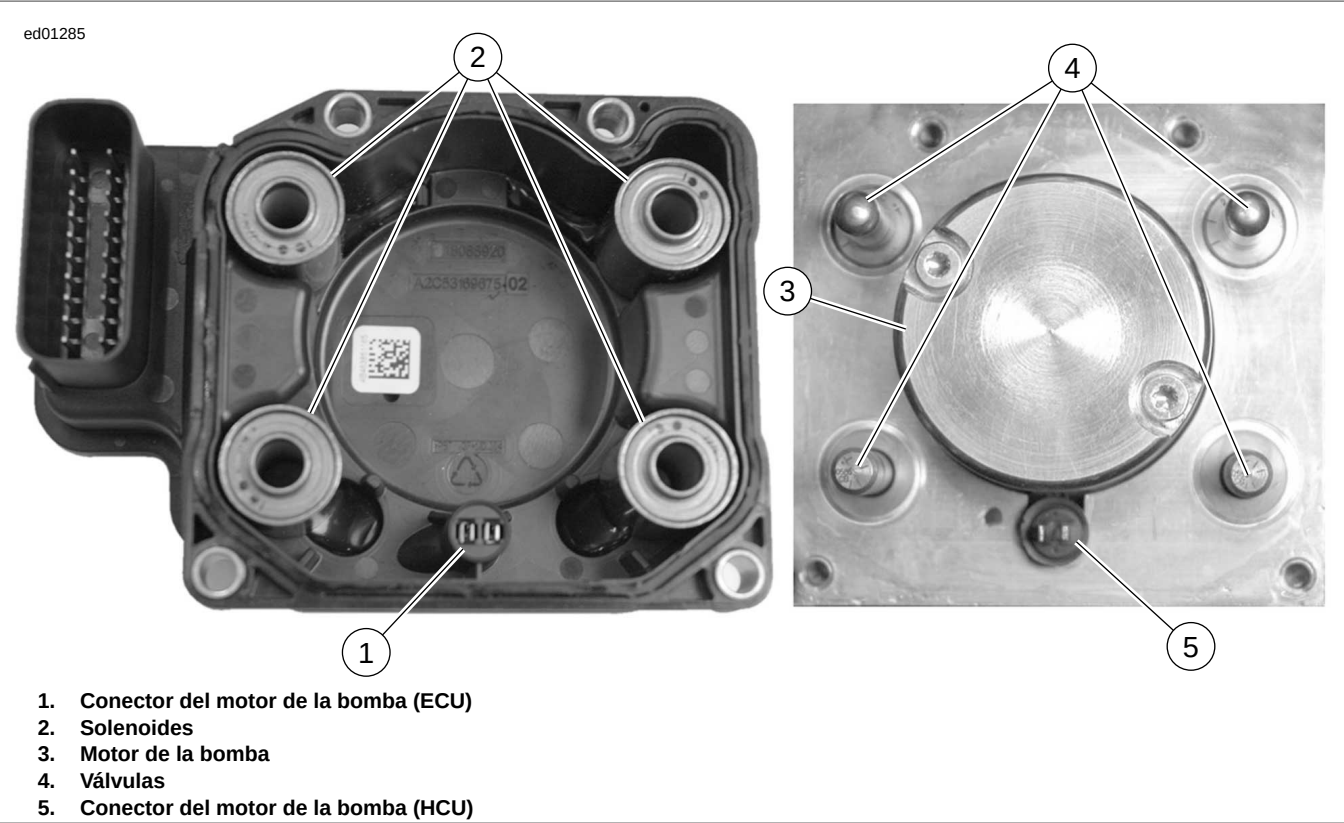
Conectores de la ECU y HCU del motor de la bomba
